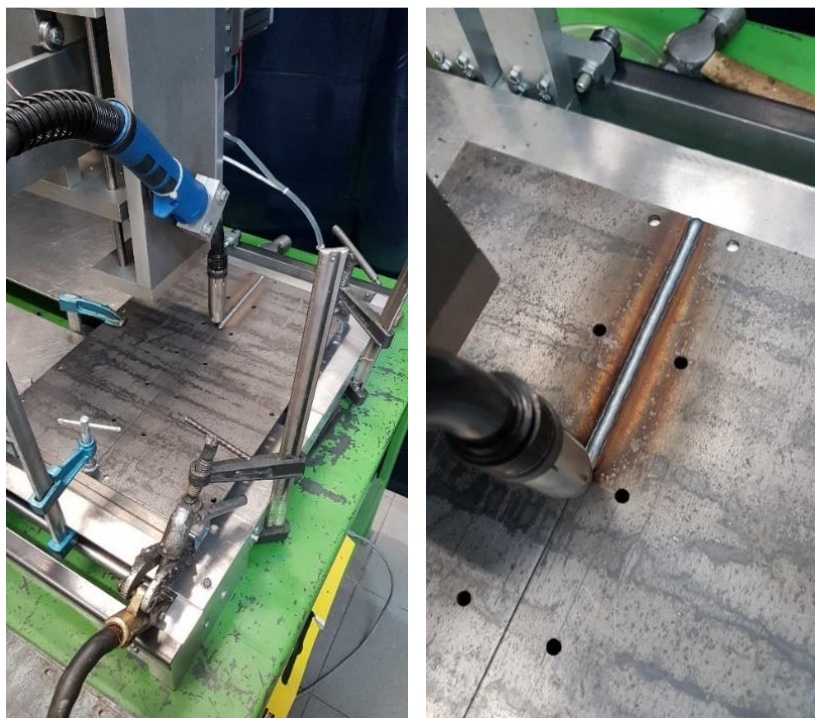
Cordão de solda topo (0°) realizado na união das chapas.
